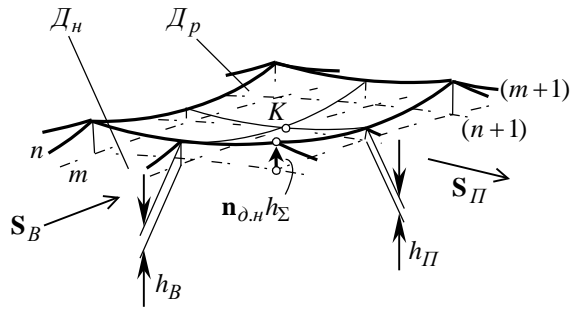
Элементарная ячейка на обработанной поверхности детали.
